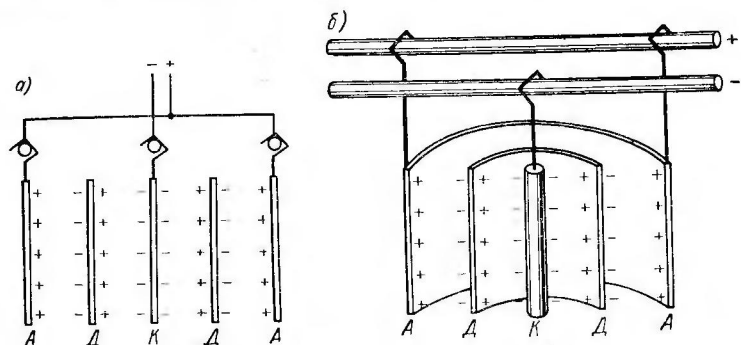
Схема биполярного способа меднения пластинчатых (а) и цилиндрических (б) деталей (А — анод; К — катод; Д — покрываемая деталь)
